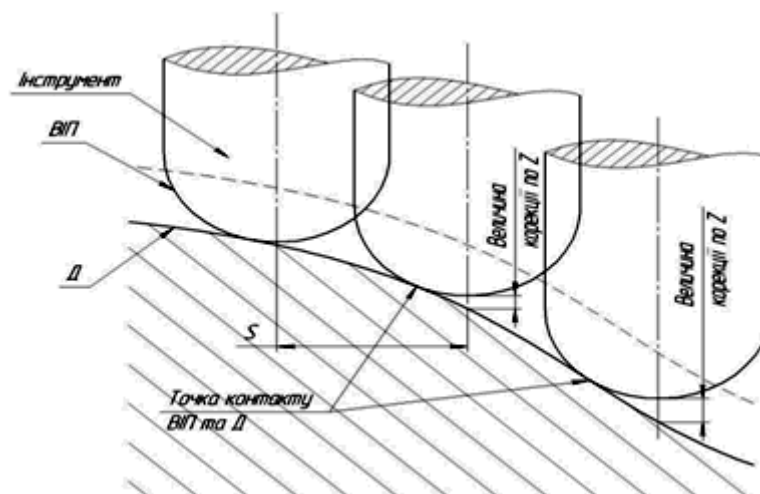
Схема обробки з витриманою величиною подачі. [13]
